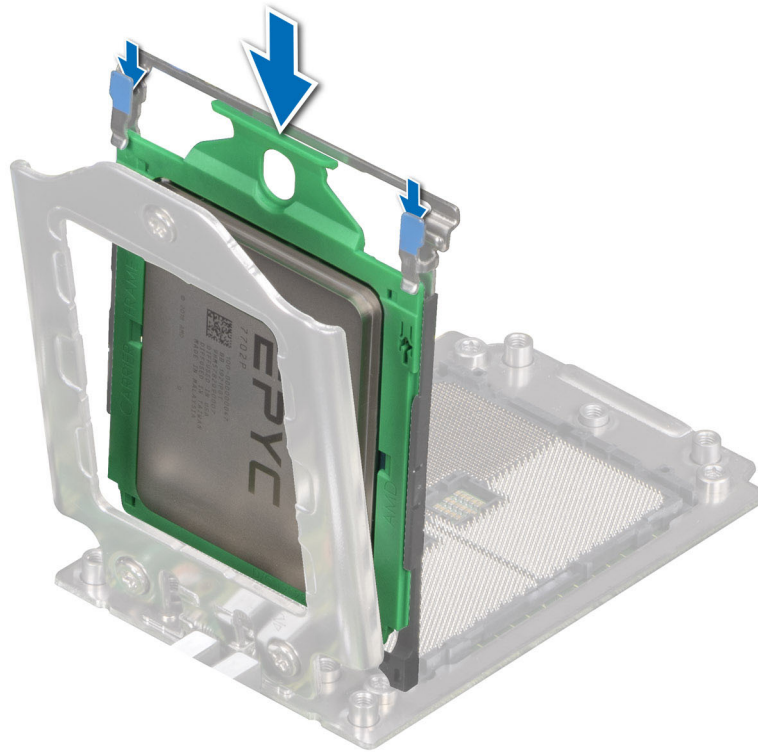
Positionnement du plateau du processeur dans le cadre à glissière
